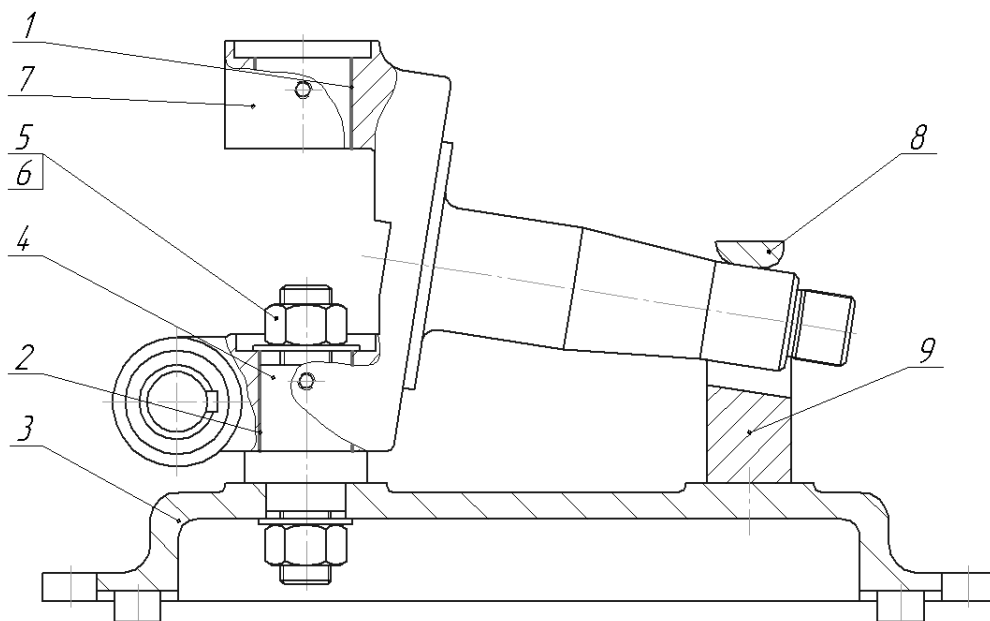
Технологическая оснастка для установления цапфы поворотной на операции растачивания: 1, 2 – отверстия, которые восстанавливаются; 3 – плита приспособления; 4 – установочный палец; 5 – шайба прижимная; 6 – гайка; 7 – цапфа поворотная; 8 – прижимная планка; 9 – призма опорная
